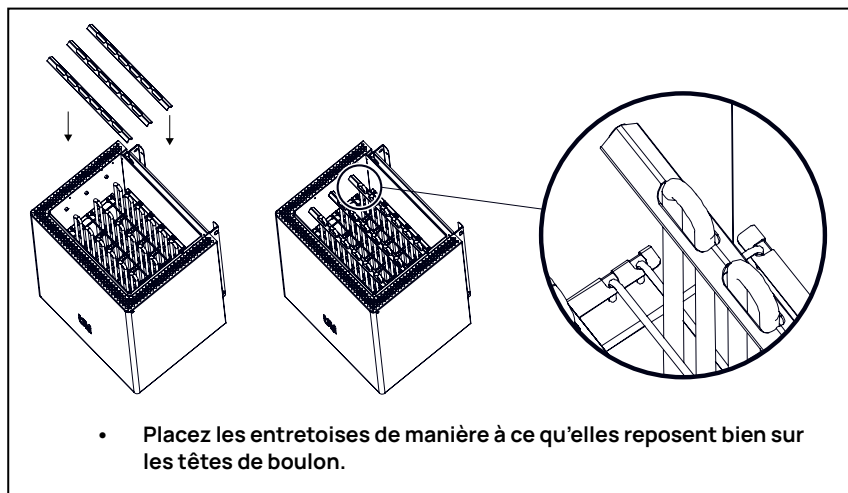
Installation de l'entretoise des éléments chauffants HUUM CORE Wall et CORE Wall Combi.
